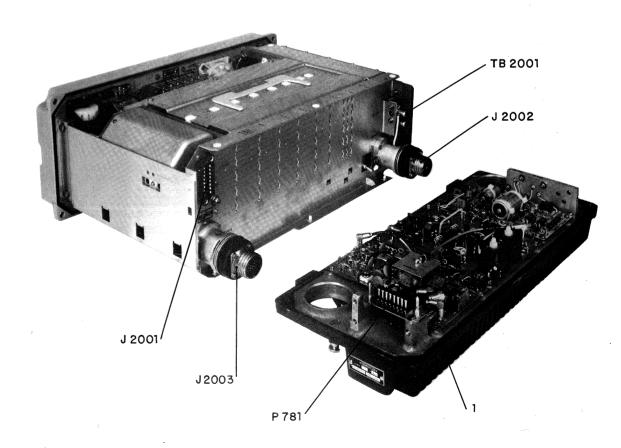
Vue arrière Fig. 2 Back view Fig. 2 Vista trasera
